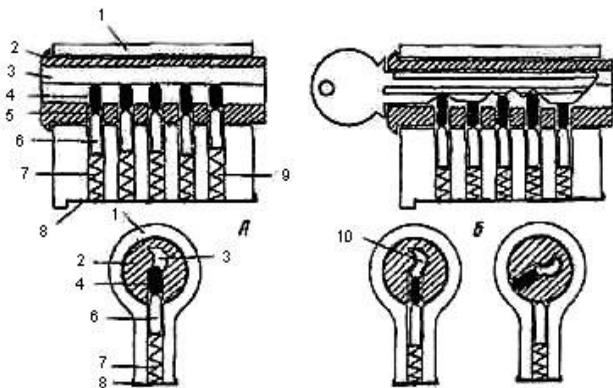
Устройство цилиндрического механизма: А — механизм в запорном положении; Б — механизм в отпертом положении; 1 — корпус; 2 — цилиндр; 3 — скважина для ключа; 4 — штифт цилиндра; 5 — гнездо цилиндра; 6 — штифт корпуса; 7 — пружина корпуса; 8 — крышка корпуса; 9 — гнездо корпуса; 10 — ключ
